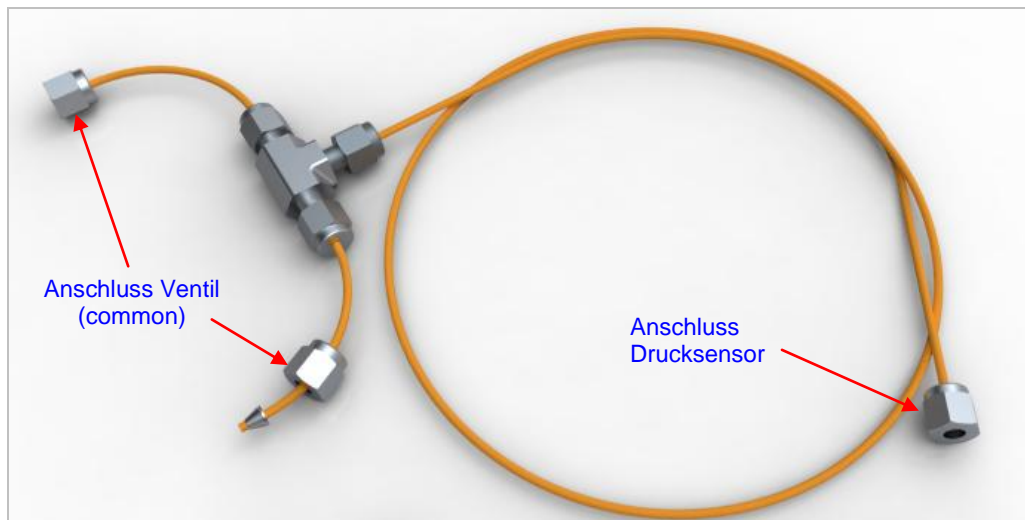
Hochdruckschlauch 1 - Drucksensor - Ventil
